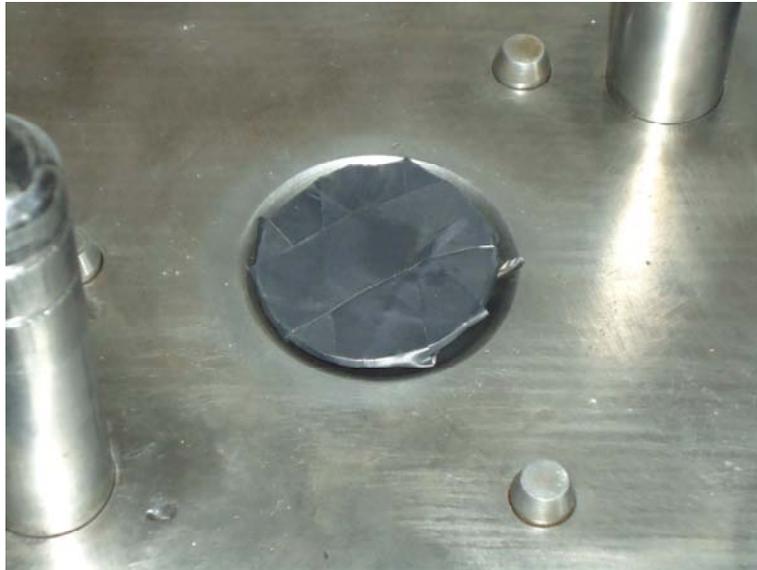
Forma de ensamblar el explosivo en la placa portadora de explosivo
